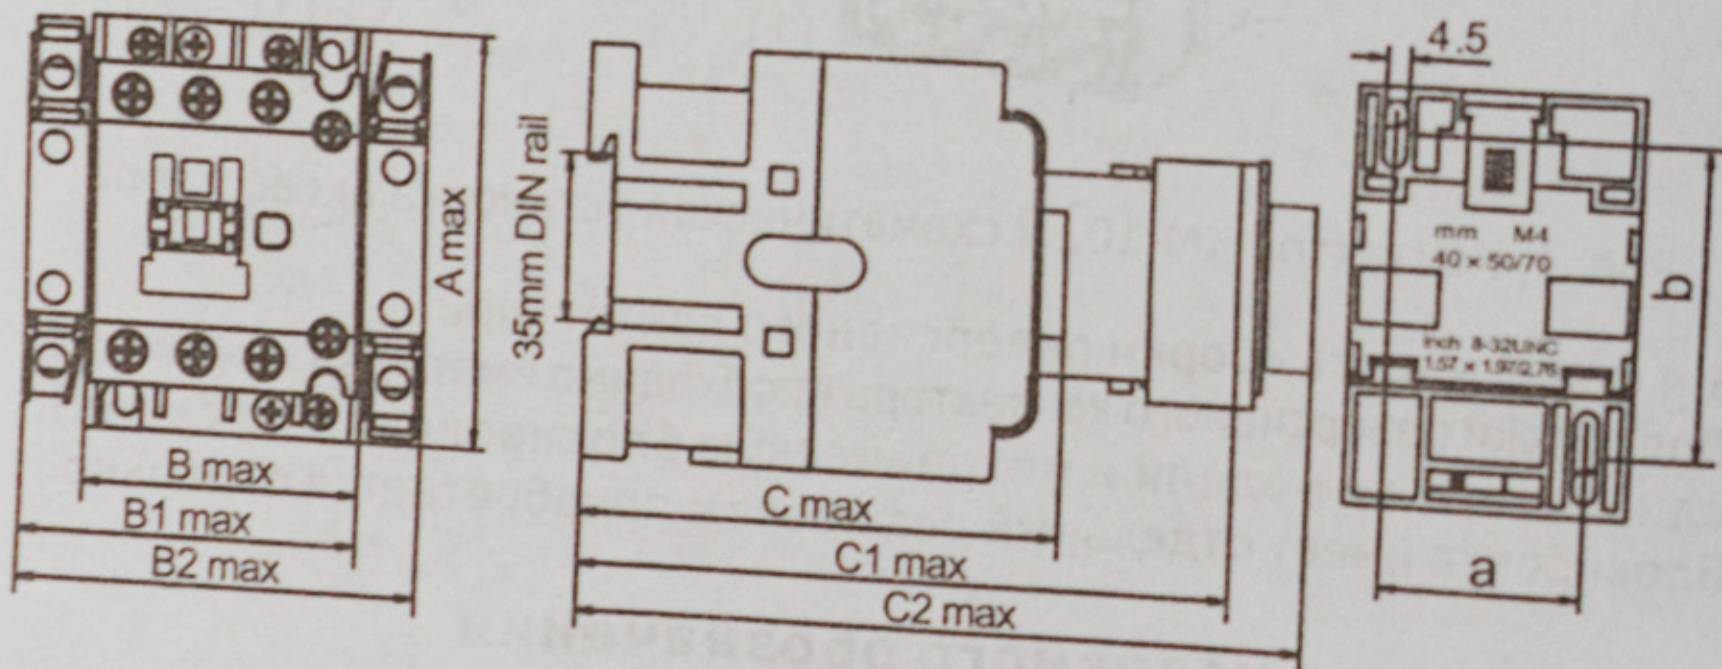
Габаритные и установочные размеры контакторов на токи 6А-38А, мм.
